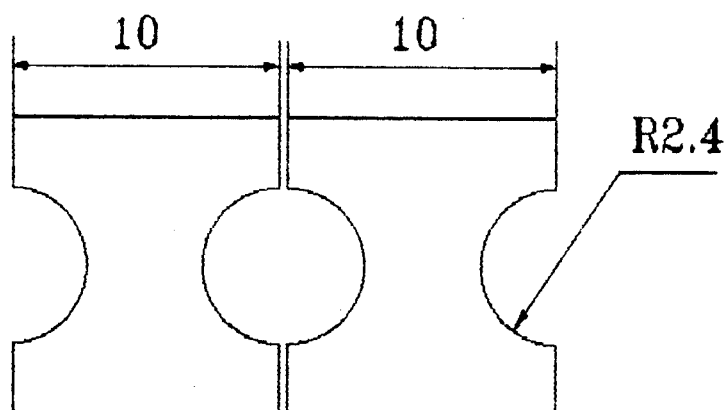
Кварцевая билинза для фокусировки нейтронов [28,29].
